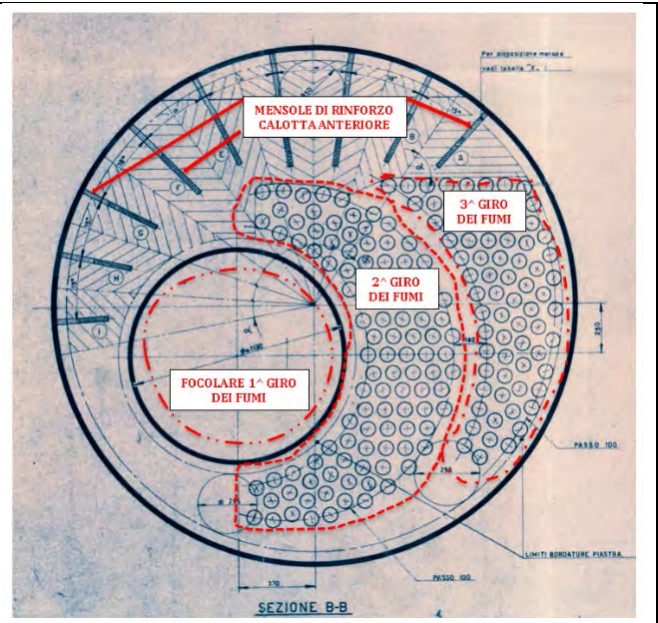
SEZIONE B-B Disposizione dei tubi da fumo per il "2^o e 3^o giro dei fumi, la disposizione delle mensole di rinforzo piastra tubiera anteriore
